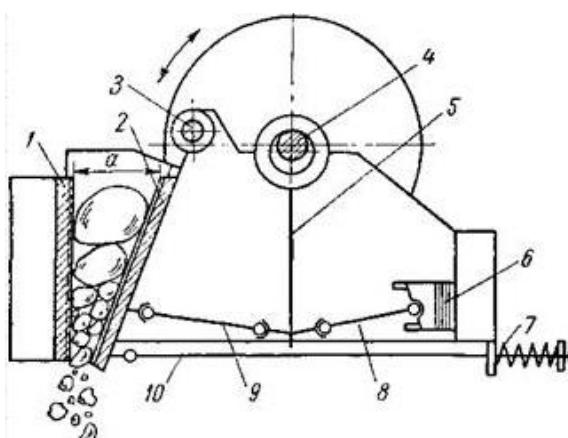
Конструктивная схема щековой дробилки: 1 - неподвижная щека; 2 - подвижная щека; 3 - ось подвески щеки; 4 - эксцентриковый вал; 5 - шатун; 6 - механизм изменения ширины разгрузочной щели; 7 - замыкающая пружина; 8 - задняя распорная плита; 9 - передняя распорная плита; 10 - тяга замыкающего устройства.
